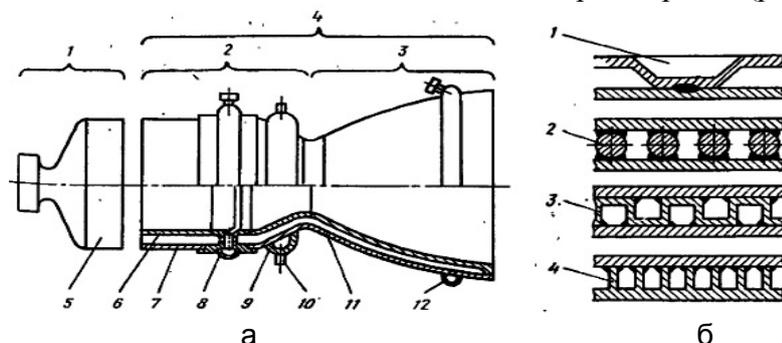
Камера ЖРД: разбивка на технологические узлы (а); способы образования каналов (б): 1 – выштамповки; 2 – спиральная проволока; 3 – гофрированные проставки; 4 – фрезерованные пазы; 5 – смесительная головка; 6 – внутренняя оболочка; 7 – наружная оболочка; 8 – пояс завесы; 9 – бандаж; 10 – цапфа; 11 – разрезное кольцо; 12 – коллектор
